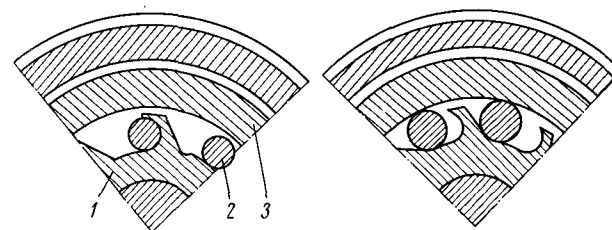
Обгонная муфта с цилиндрическими роликами пускового двигателя установки ГТ-700-4 НЗЛ
